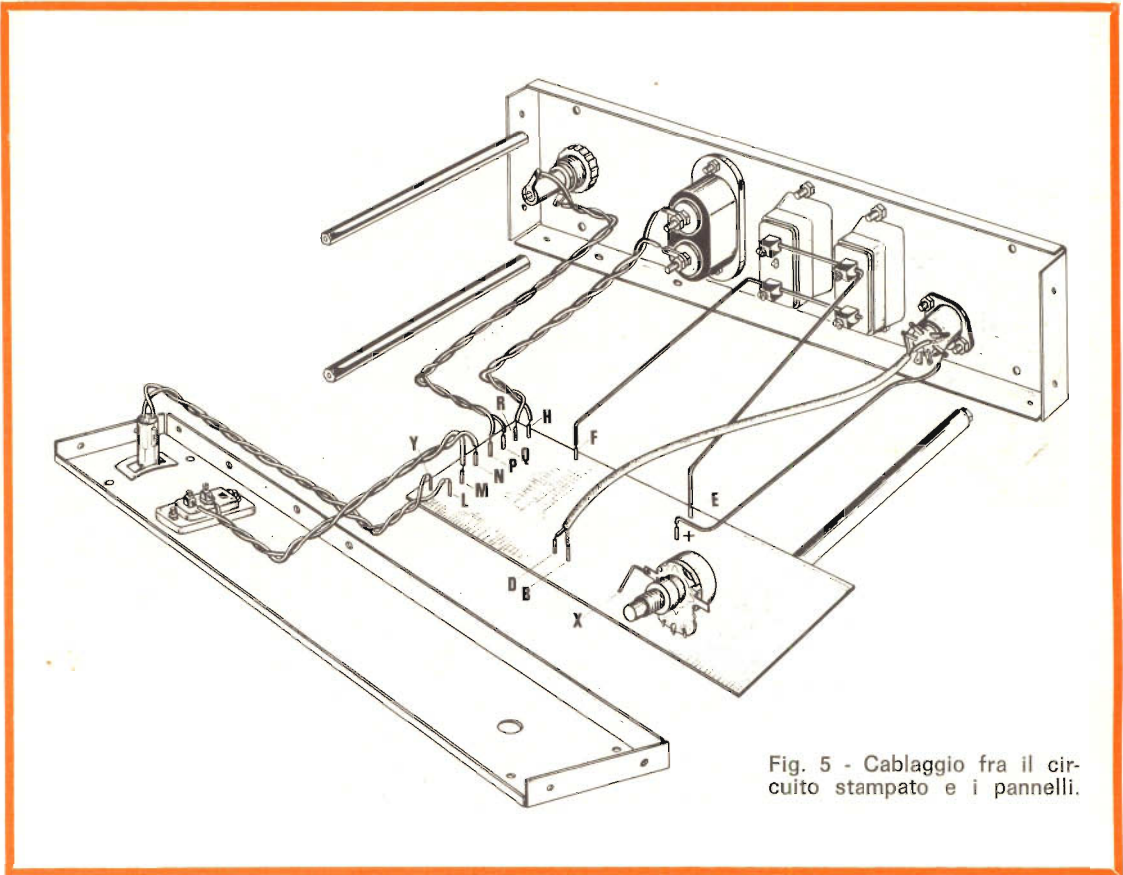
Cablaggio fra il circuito stampato e i pannelli.
